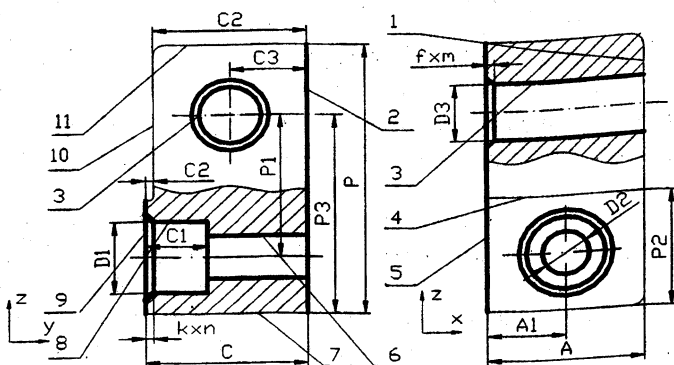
Чертеж детали, графы размерных связей и угловых расположений
